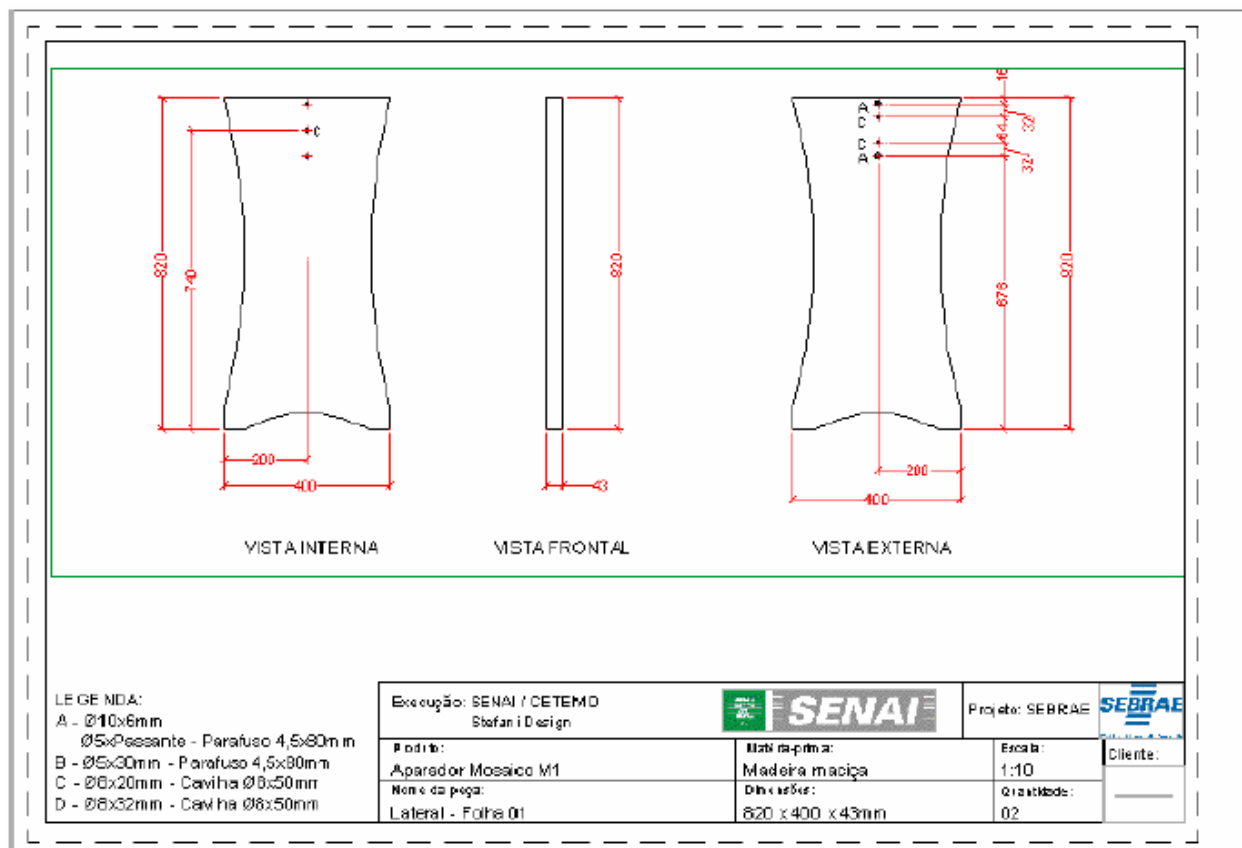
Desenho técnico de AutoCAD - Projeto Móveis do Pampa.
